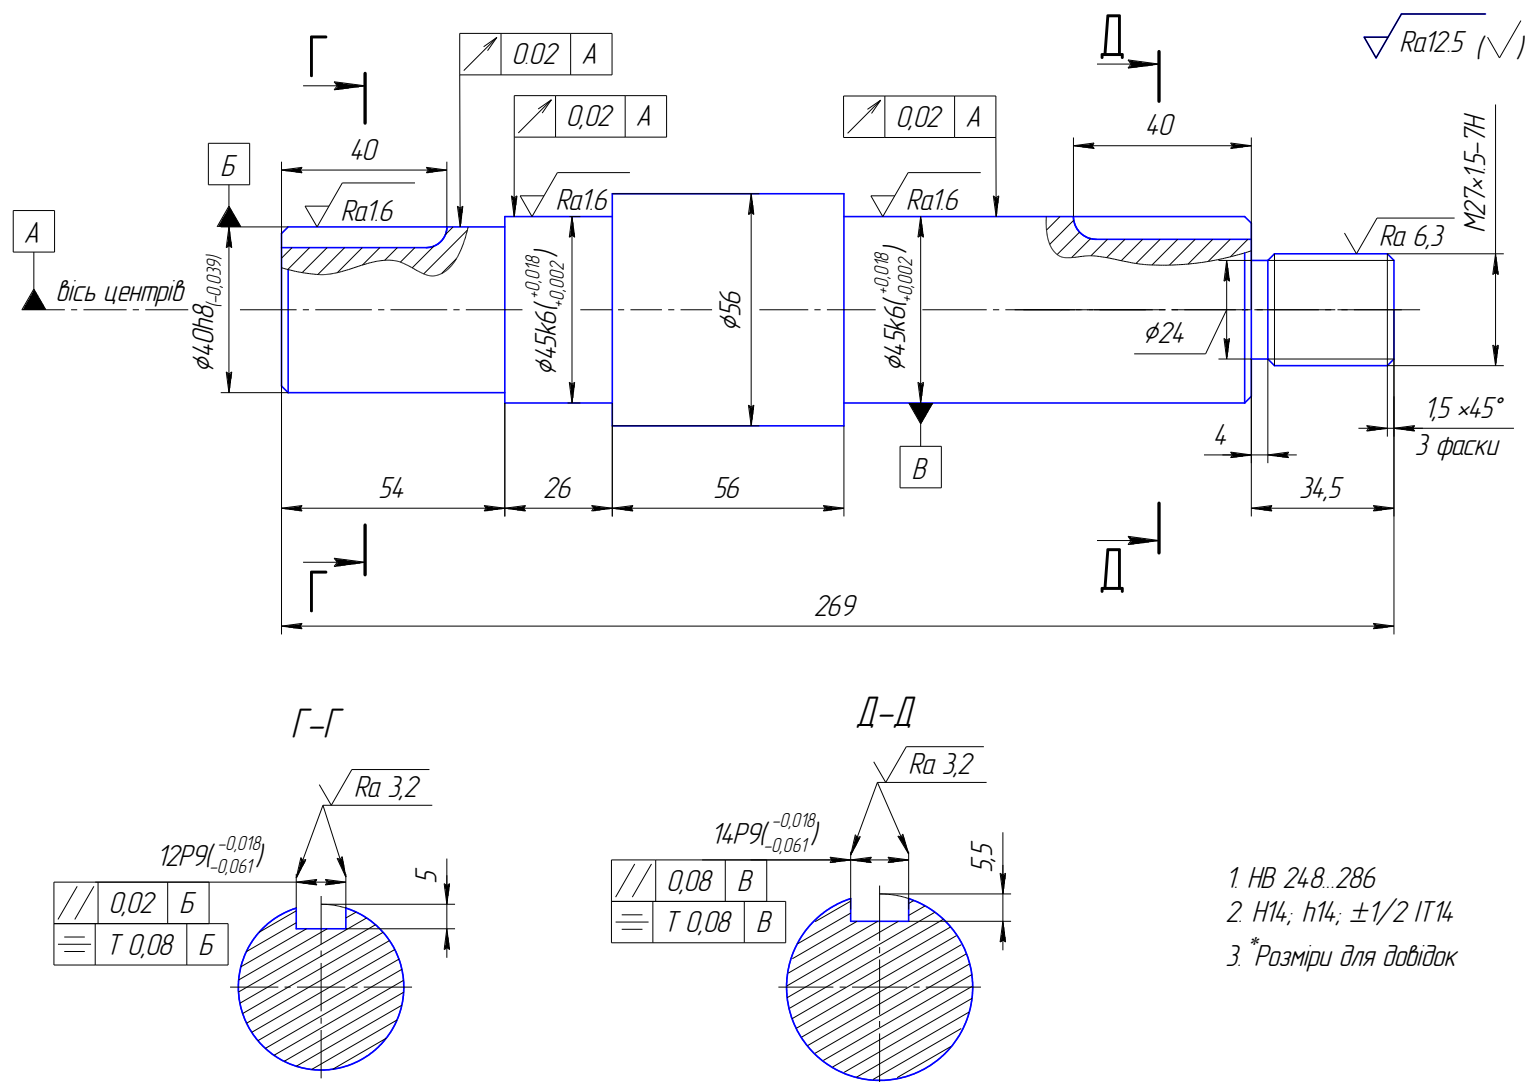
Ескіз до прикладу визначення кількості ступенів обробки поверхні заготовки деталі типу «ступінчастий вал»
